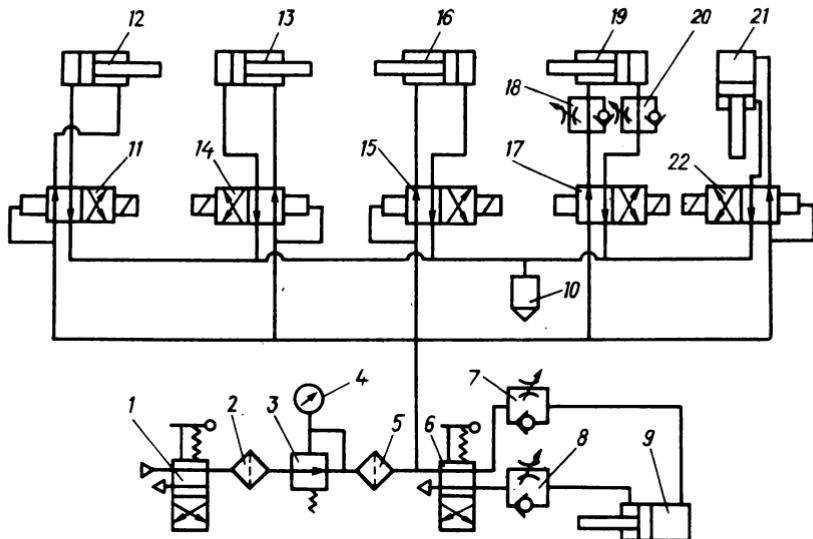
Схема пневматической системы лущильного станка ЛУ17-10
